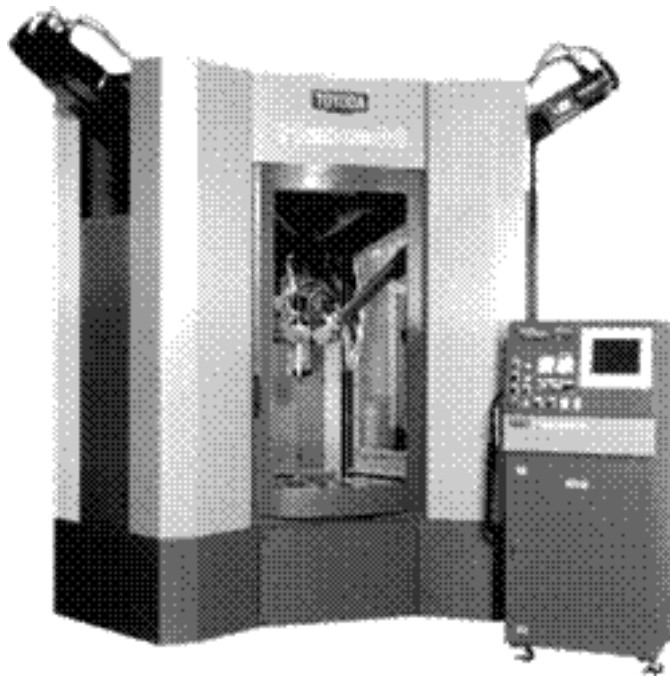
Широкоуніверсальний обробний центр Неха фірми Toyota Machine Works
